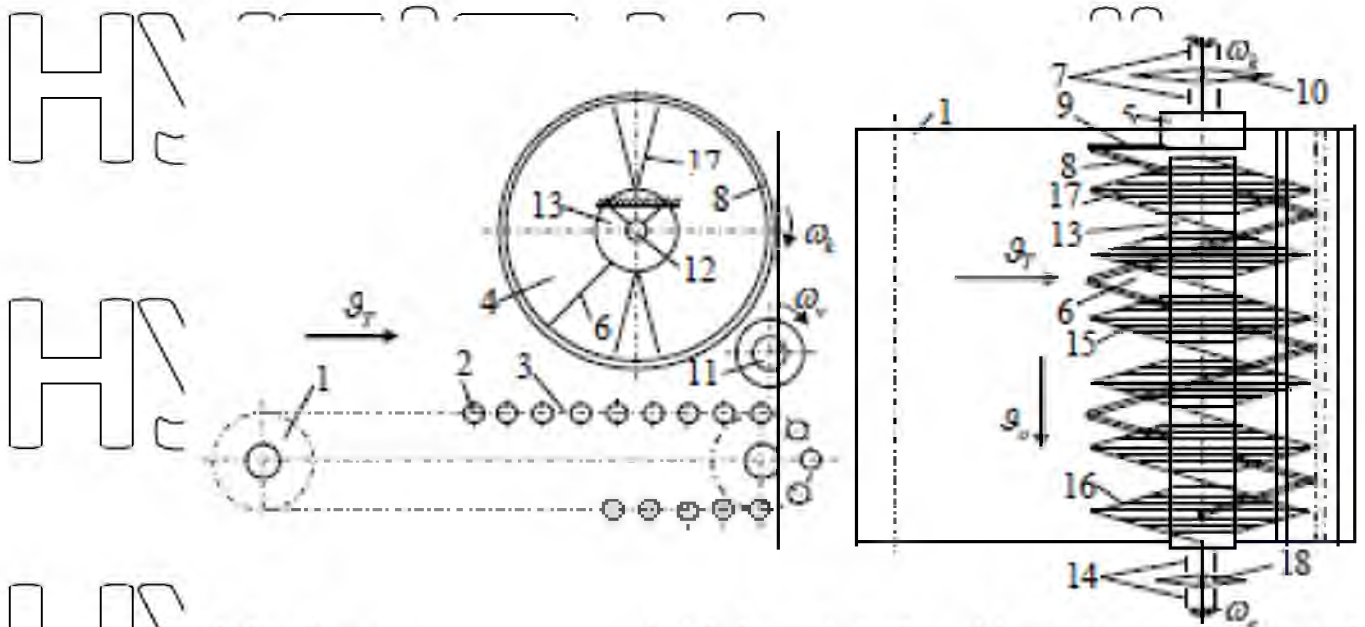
Конструктивна схема очисника вороху: 1 – подавальний транспортер; 2 – пруток; 3 – робоча гілка; 4 – комбінований робочий орган; 5 – пустотілий гвинтовий циліндр; 6 – виток; 7, 14 – опора; 8 – труба; 9 – фланець; 10, 18 – зірочка; 11 – відкидний валець; 12 – приводний вал; 13 – барабан; 15, 16 – гвинтова лінія; 17 – очисні елементи.
